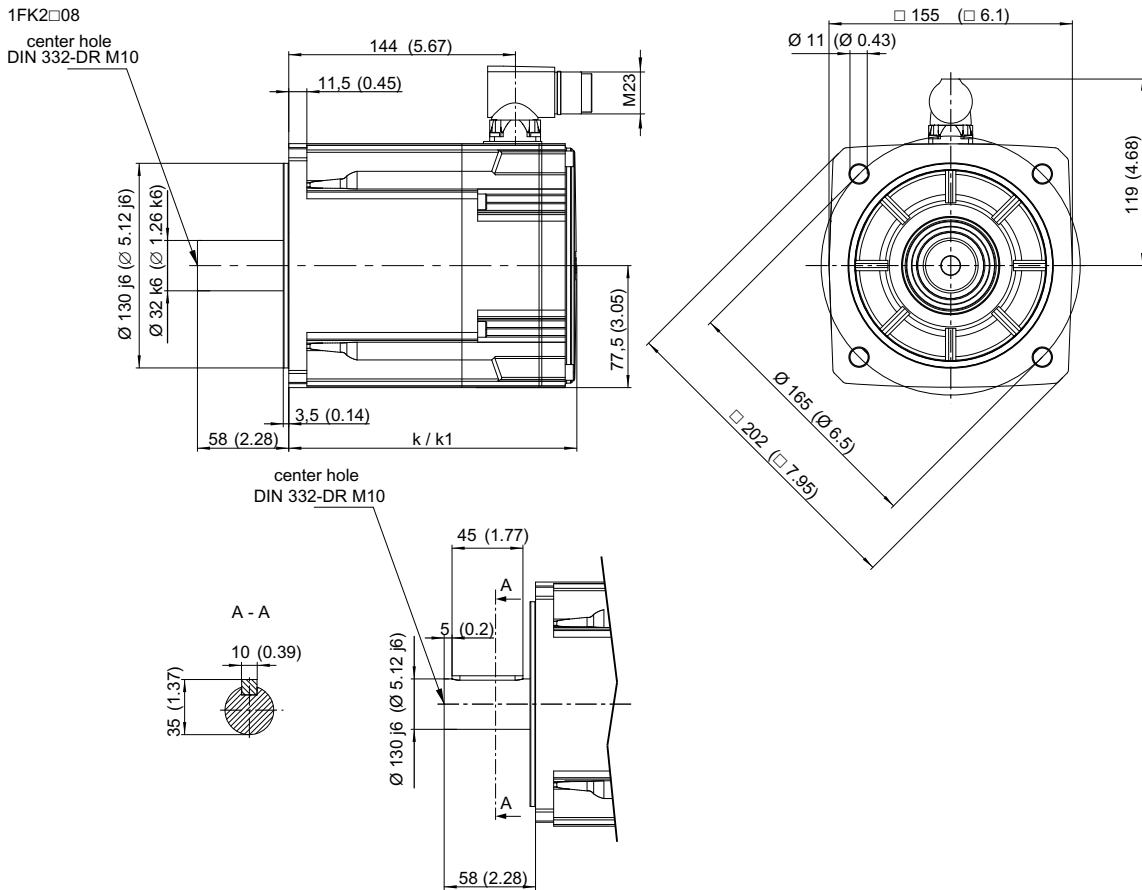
Maßzeichnung_1FK2208-3AF00
